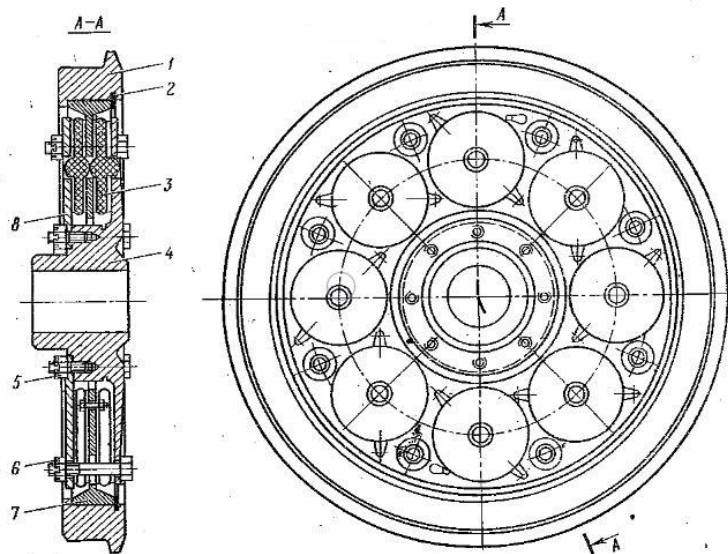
Підрезинене колесо вагона РВЗ-6М: 1- бандаж; 2 - стопорне кільце; 3- гумові вкладиші; 4- сталевий диск; 5,6- болти; 7- колісний центр; 8 - натискний диск.
